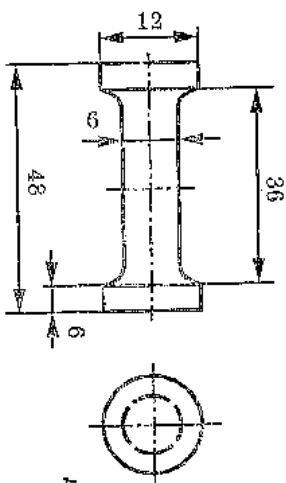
Образец для испытаний механических свойств наплавленного металла
